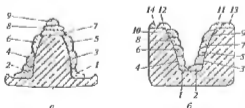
Схема наплавки отдельными валиками фасонных поверхностей:
